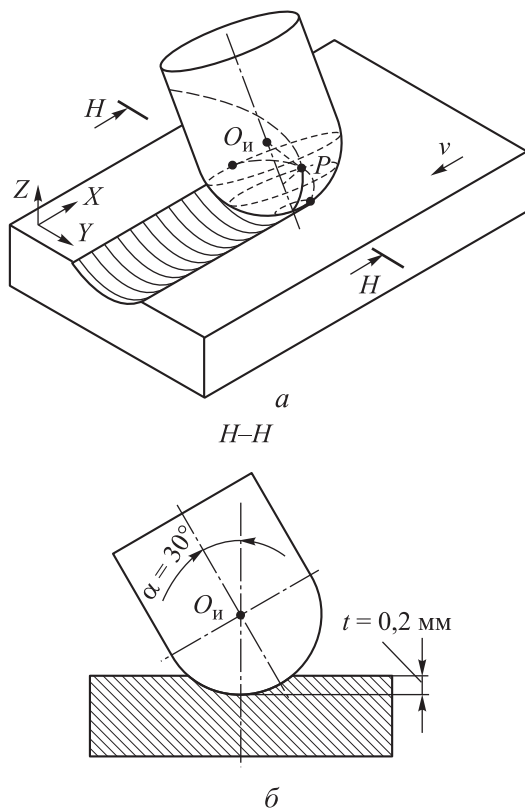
Схемы обработки детали (а) и проходящего через нормаль к образуемой поверхности осевого сечения КРФ (б):
